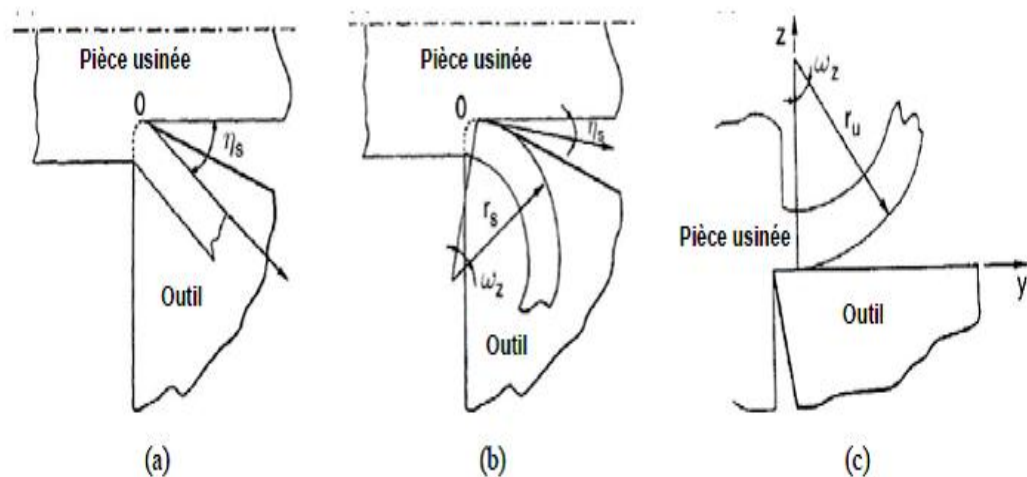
Trois formes basiques des copeaux (a) copeau droit, (b) copeau courbé dans le plan de la face de coupe, (c) copeau courbé dans le plan orthogonal à la face de coupe, [4]
